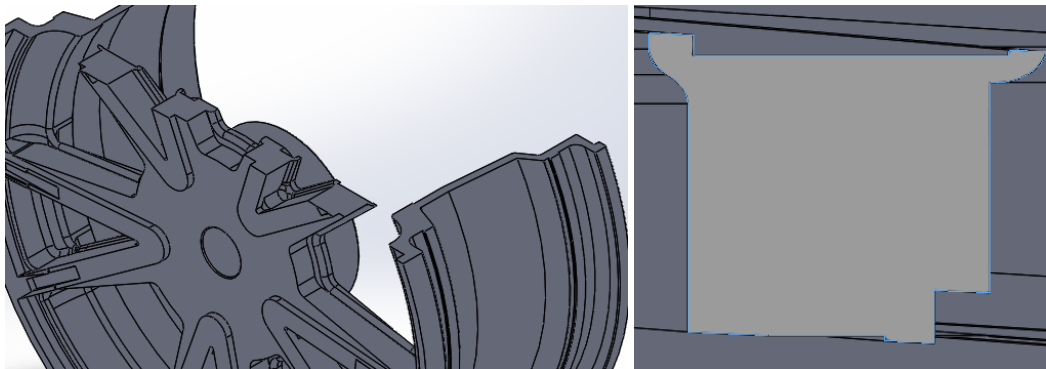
Sección más desfavorable de la llanta desarrollada.
